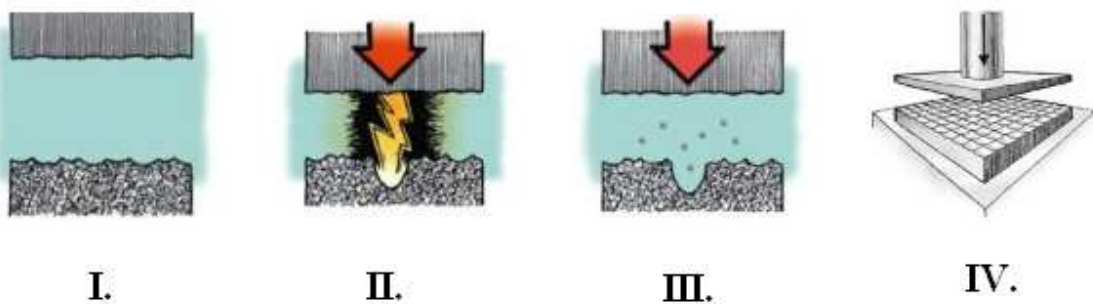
Princip elektroerozivního obrábění [12]
